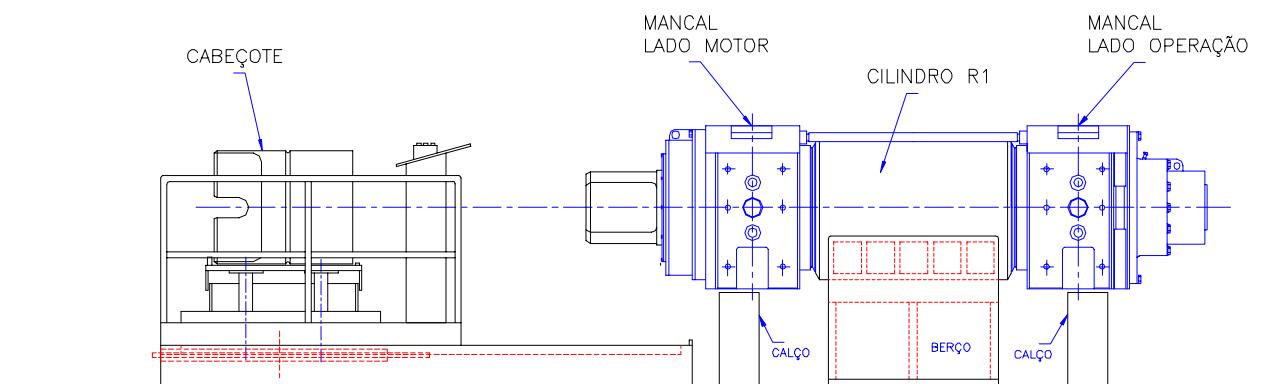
Dispositivo de montagem/desmontagem de cabeçotes (Desmontagem).
